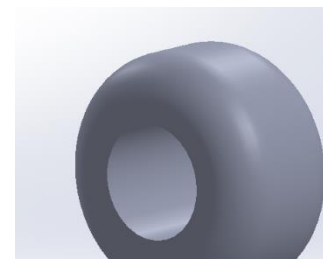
Vista de pieza N°19 (Fuente 107)
